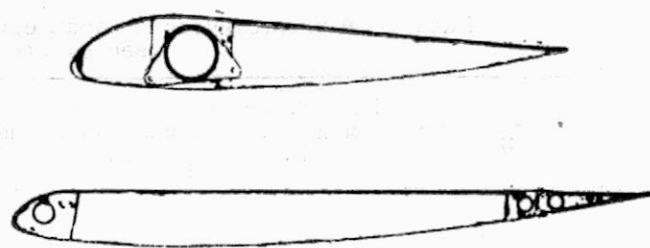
Профили крыла (вверху) и стабилизатора (внизу)
